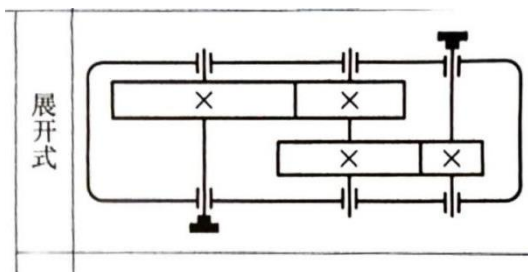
二级直齿圆柱齿轮减速器 (展开式) 结构简图
